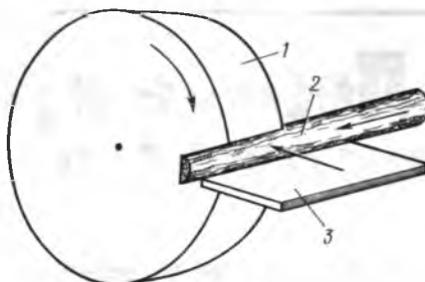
Обработка древесного керна быстровращающимся точильным кругом (электроточило — без защитного кожуха, керн — без металлической трубки):
